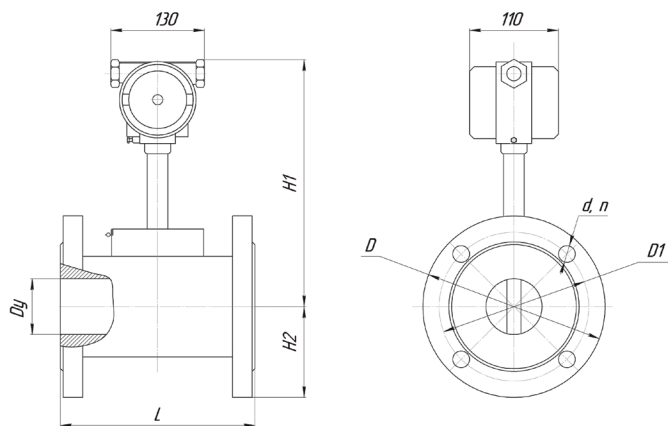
Габаритные и присоединительные размеры для преобразователя Тирэс фланцевого конструктива (исполнение А) температурного исполнения Т1.
